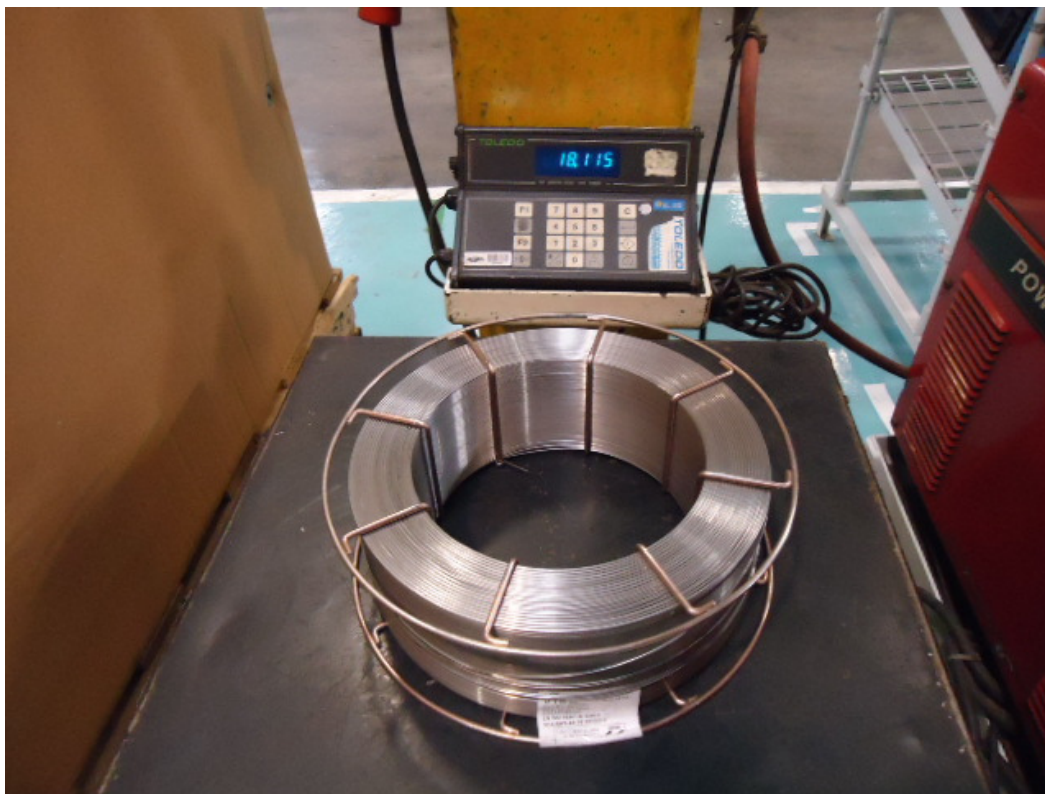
Arame após a soldagem com mistura 25% CO₂
